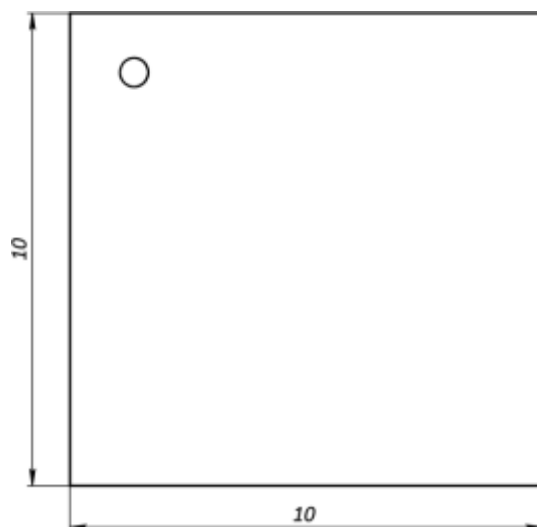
Габаритные размеры корпуса микроконтроллера (вид сверху)
